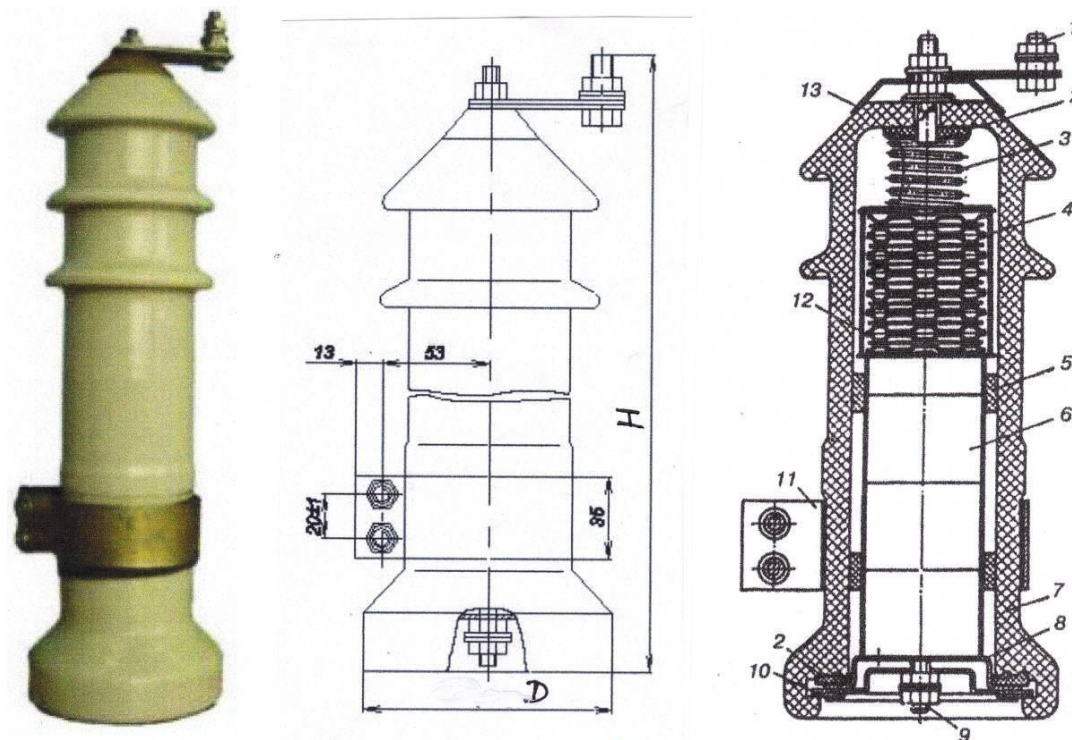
Внешний вид и конструктивная схема вентильного разрядника РВО-10
